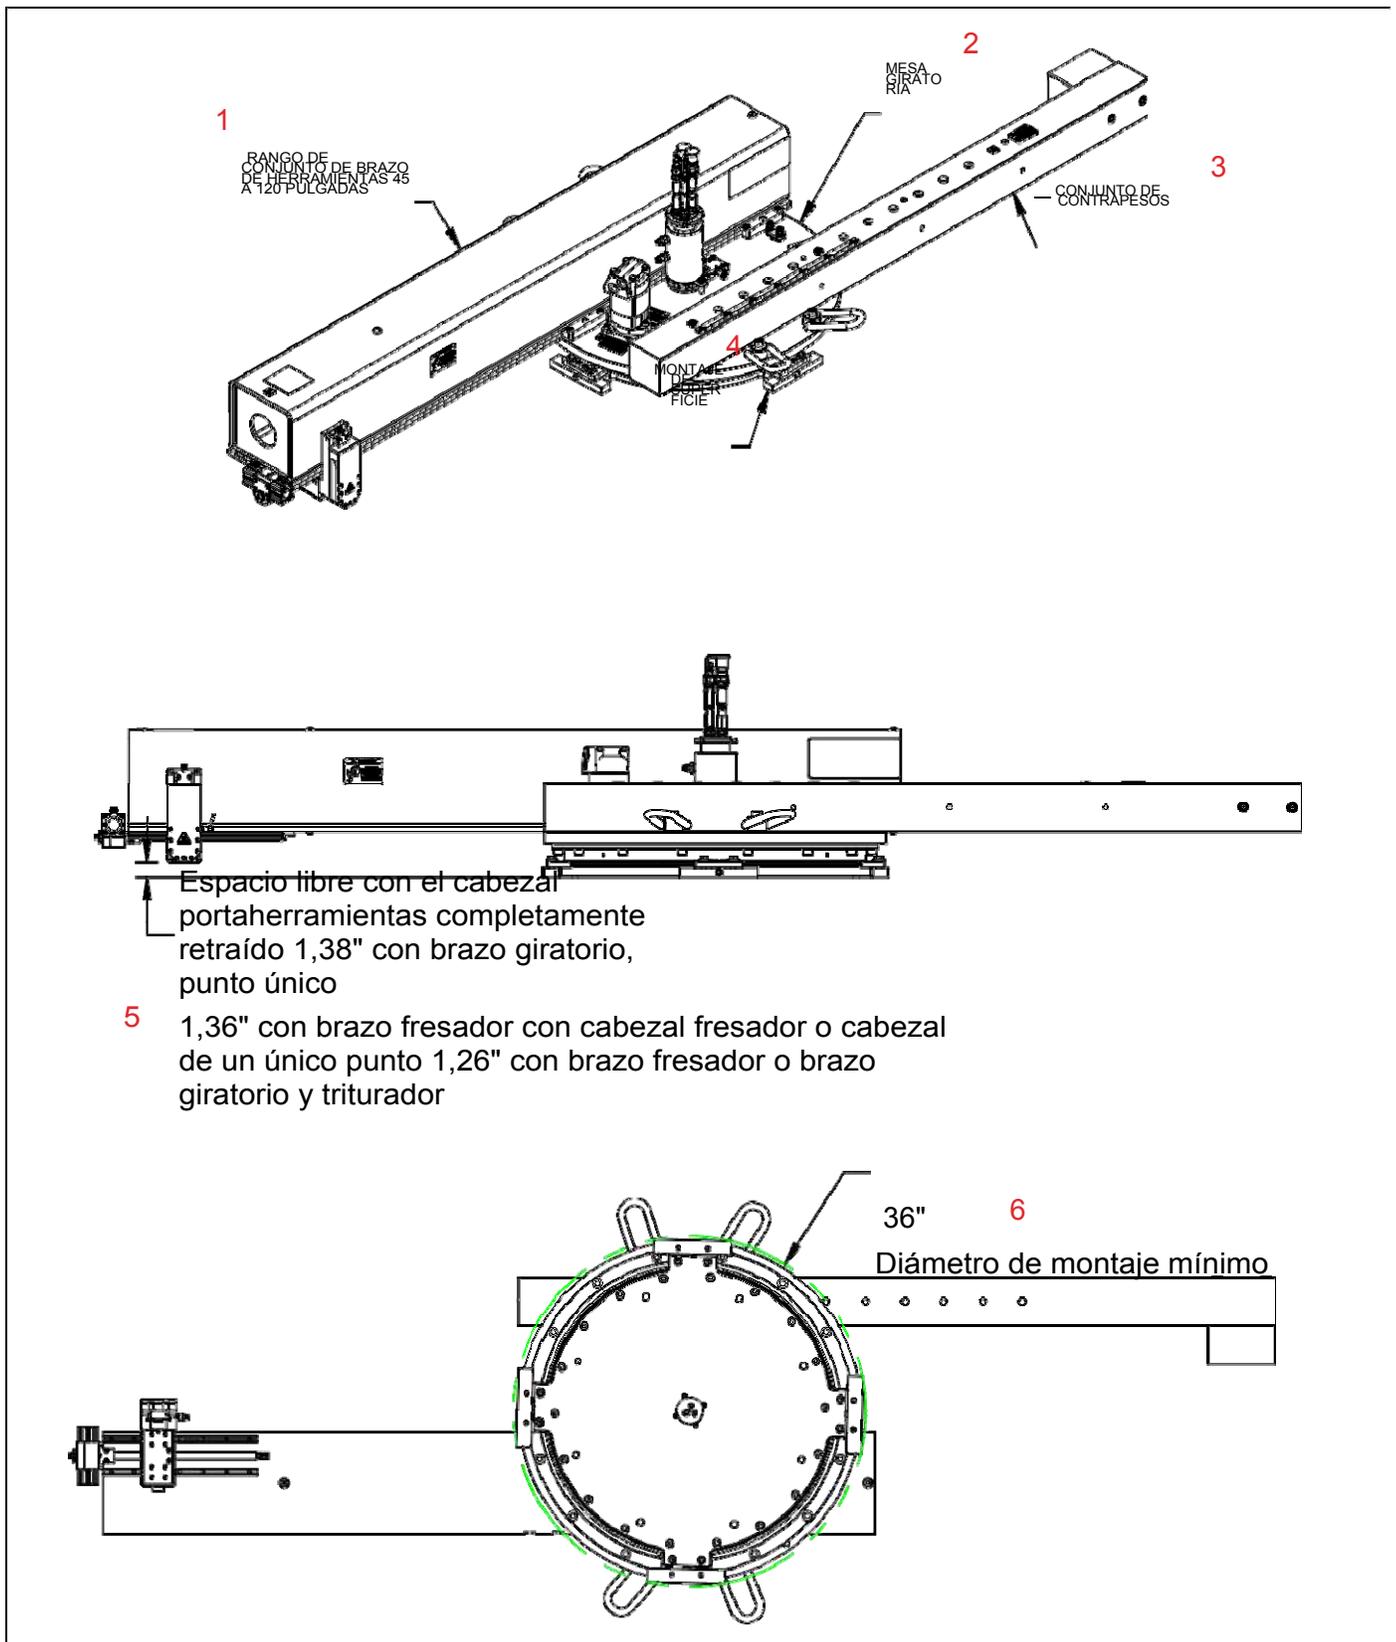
DIMENSIONES DE LA SUPERFICIE DE MONTAJE DE PUNTO ÚNICO
